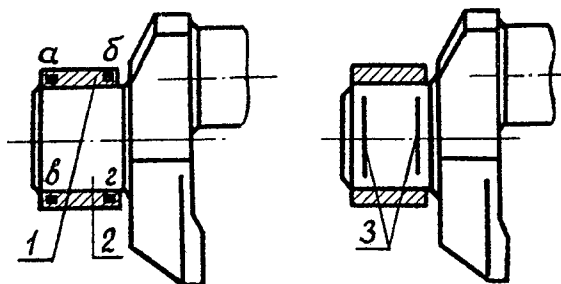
Расположение свинцовых кубиков на вкладышах коренных подшипников и свинцовых проволочек на шейке вала.
